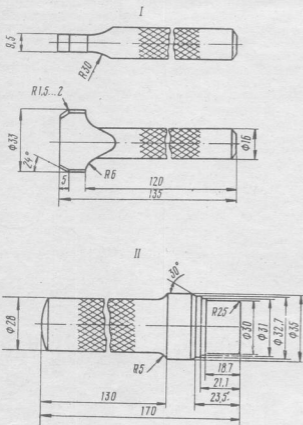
Оправки для установки заглушки в шатунной шейке коленчатого вала:
